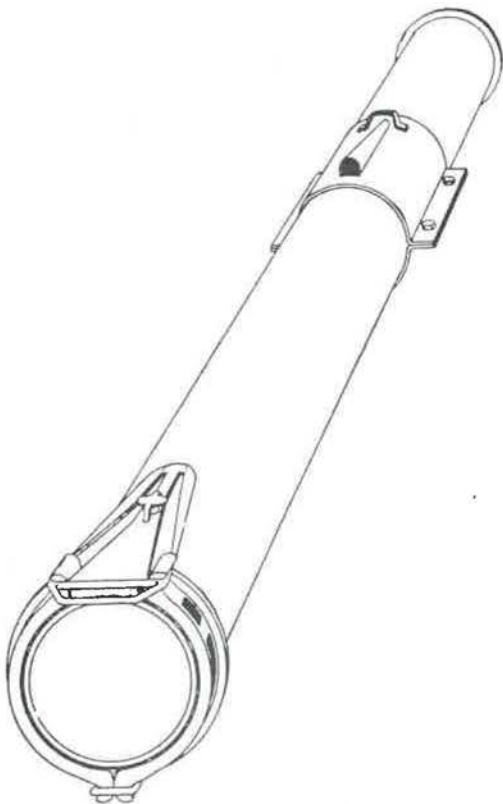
Tuyau pour remblayage par coulée de la firme Esser-Werke.
